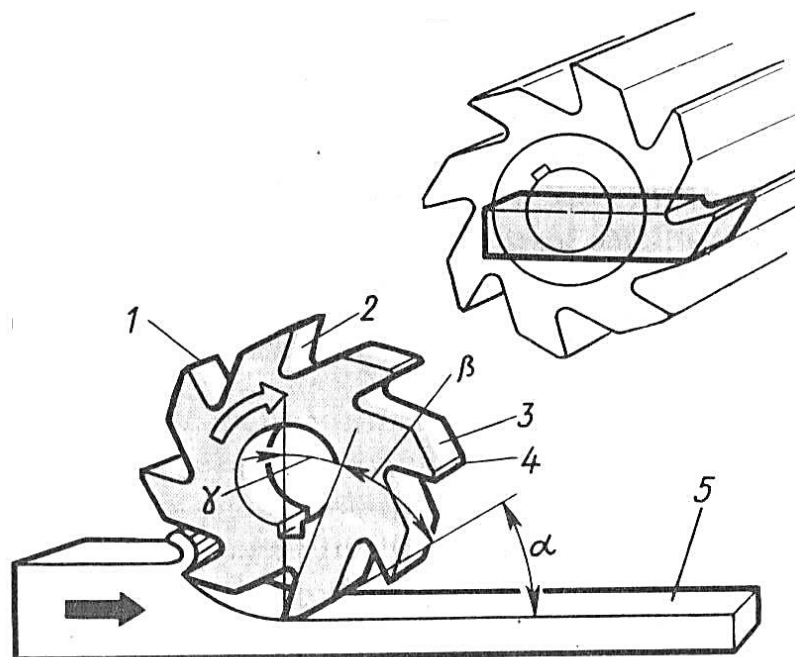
Элементы, поверхности и геометрические параметры фрезы: 1 – главная режущая кромка; 2 – передняя поверхность; 3 – задняя поверхность; 4 – ленточка; 5 – обработанная поверхность;  $\alpha$  – главный задний угол;  $\gamma$  – передний угол;  $\beta$  – угол заострения
